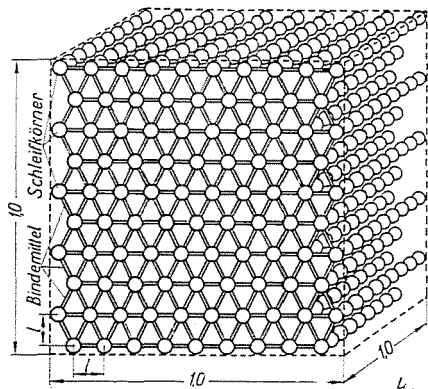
Prinzipieller Aufbau der Schleifwerkzeuge (nach MASSLOW)
